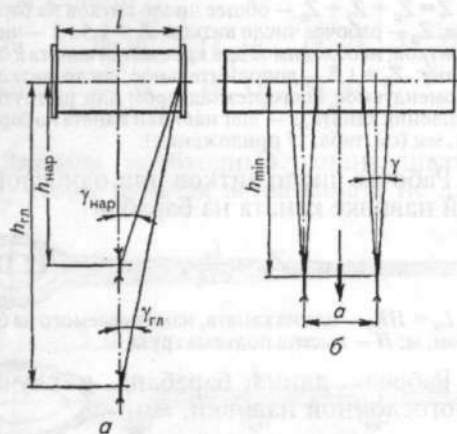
Схема к определению допустимых углов набегающего каната на барабан:
